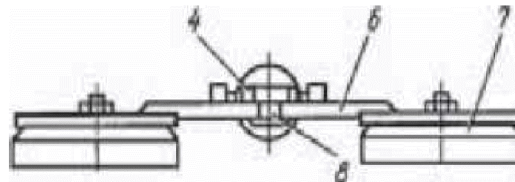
Захватний пристрій електромагнітного типу
